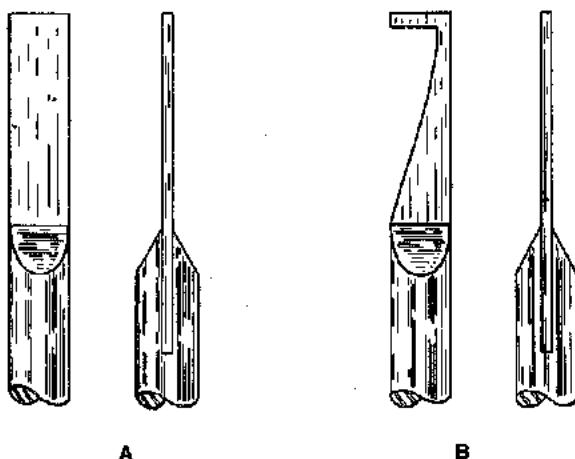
Apoyos de diente: (A) plano; (B) de gancho.
